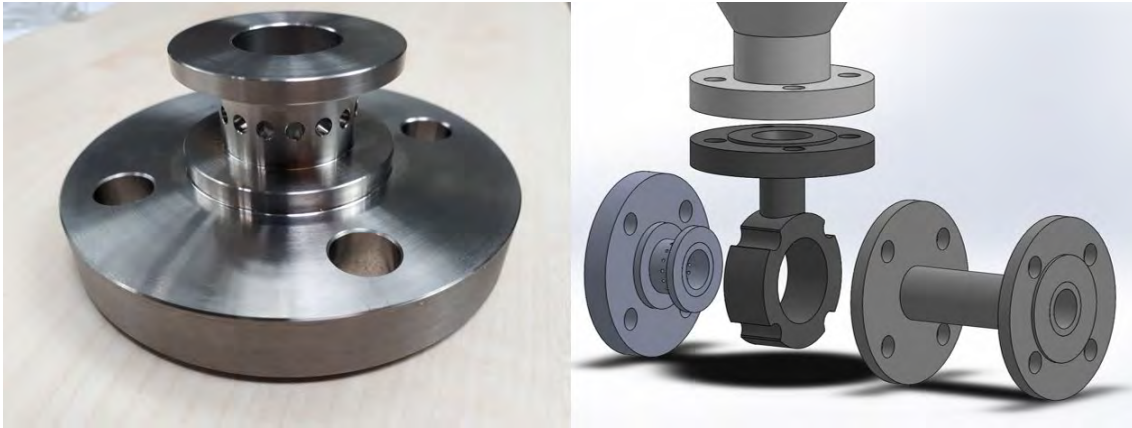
Bild sowie technische Zeichnung des Dosierrings, mit dem Partikel in das Auslassrohr hineingegeben werden können /TUD 22/
